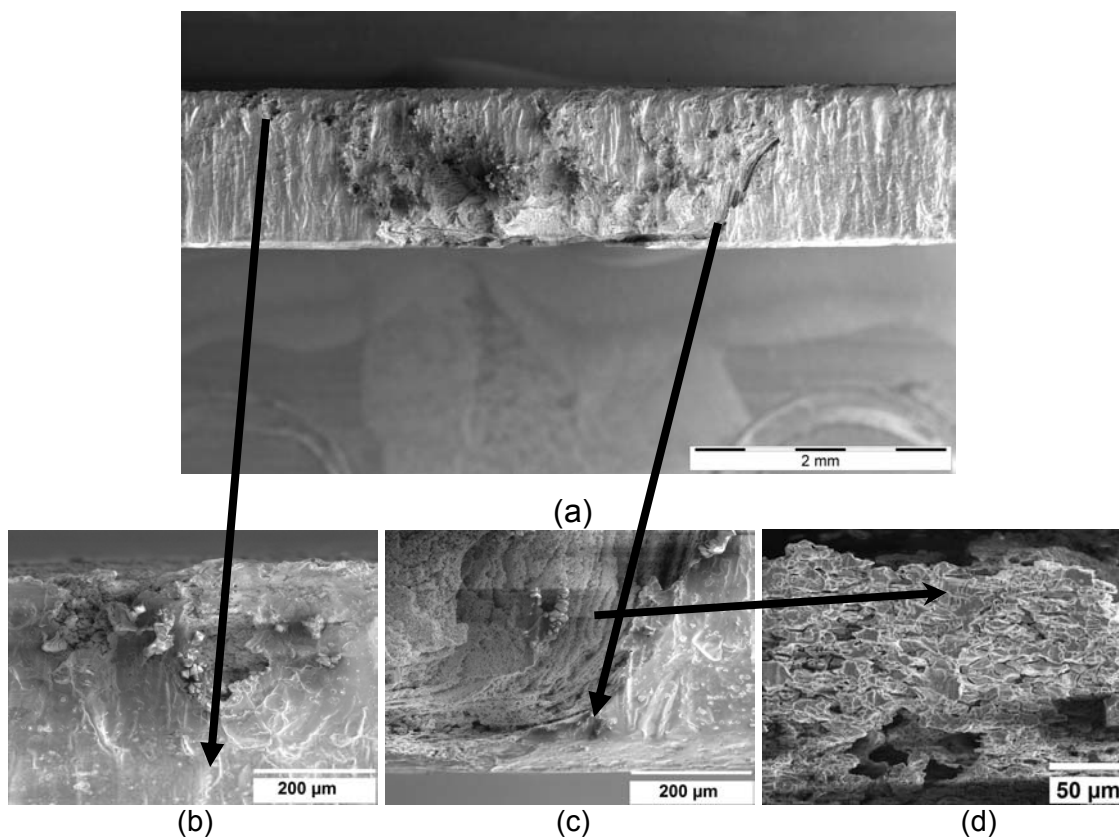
Junta soldada por FSW da liga 2024-T351 após ensaio de corrosão intergranular; (a) seção transversal da junta soldada, (b) face da solda com ataque localizado, (c) interface entre o metal base e a junta soldada e (d) ataque de corrosão intergranular na ZTMA.
